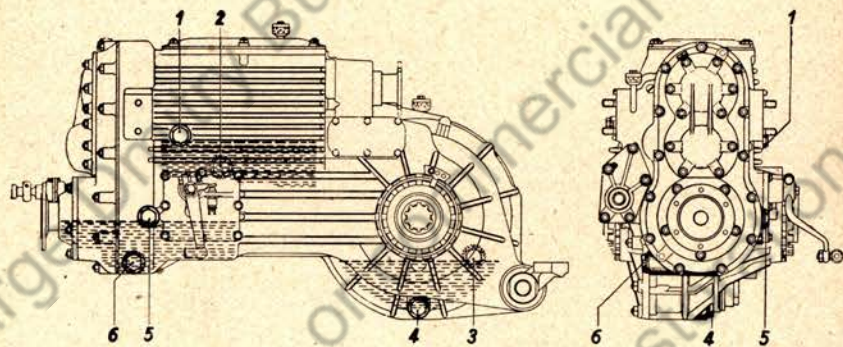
Schmierung des Wechselgetriebes (3 Öläder)
